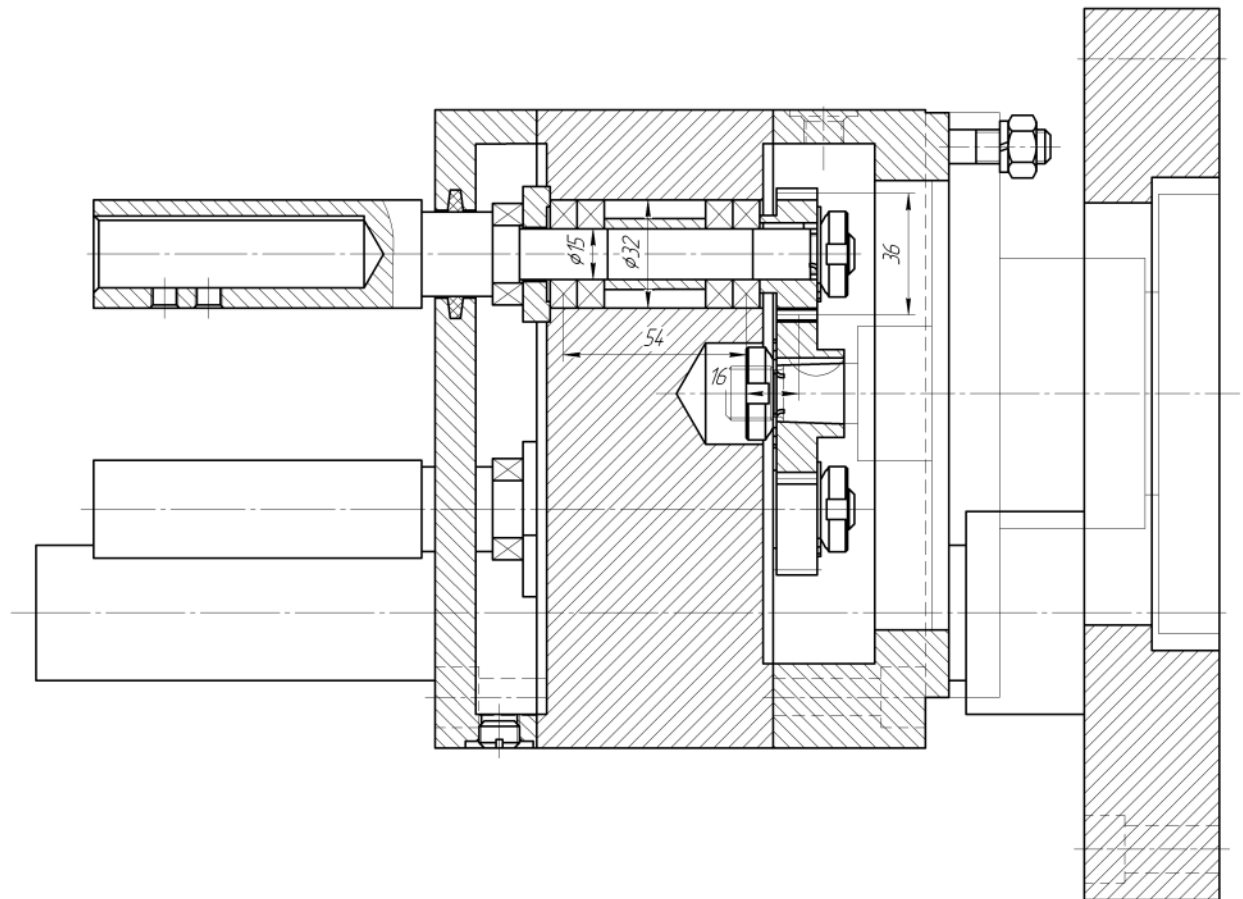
Багатошпindelна насадка до агрегатного верстата
